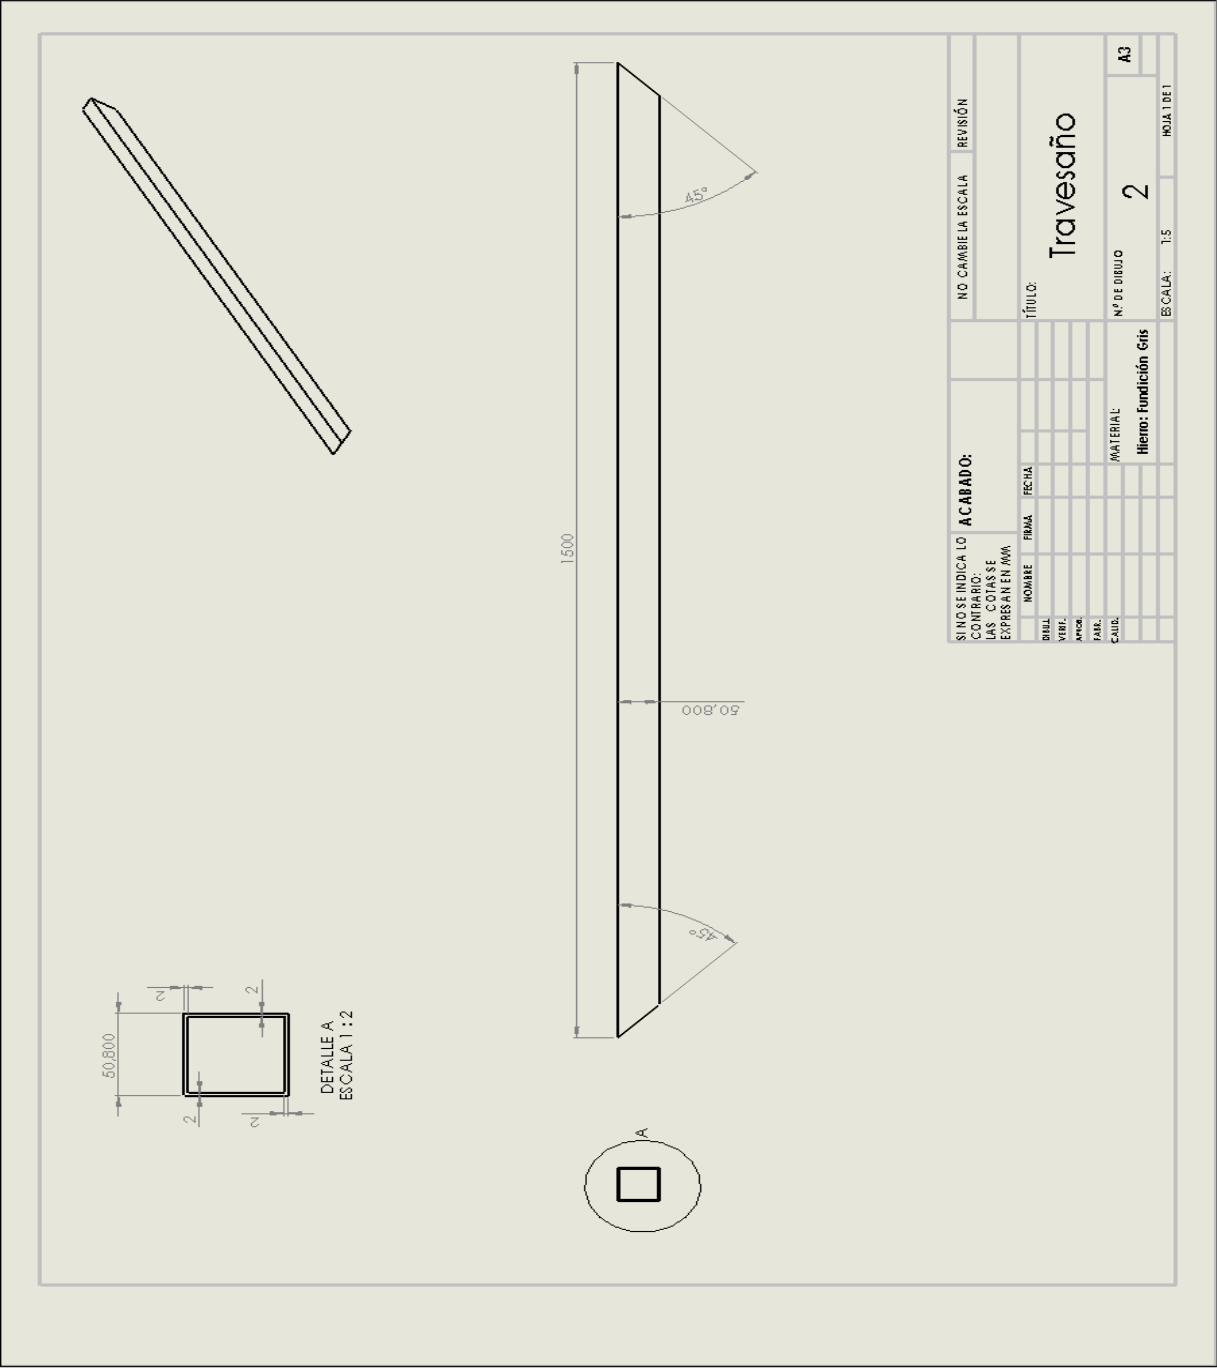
Plano de fabricación del travesaño y de la base trasera.
